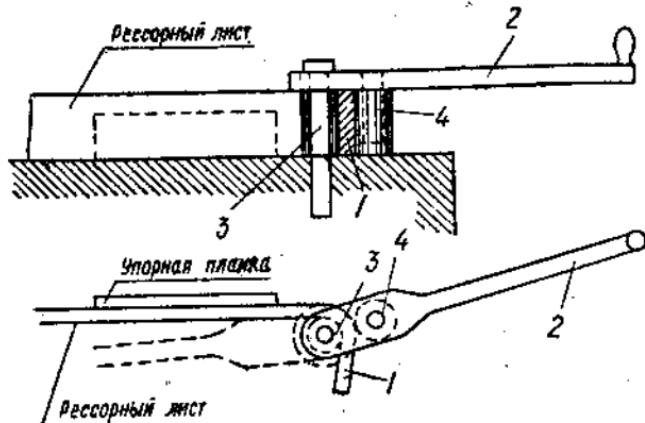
Приспособление для загибания ушка коренного листа рессоры.
